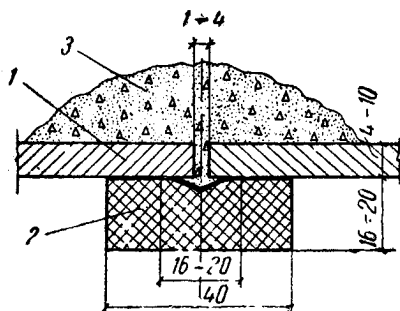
Схема сварки на флюсомедной подкладке.
